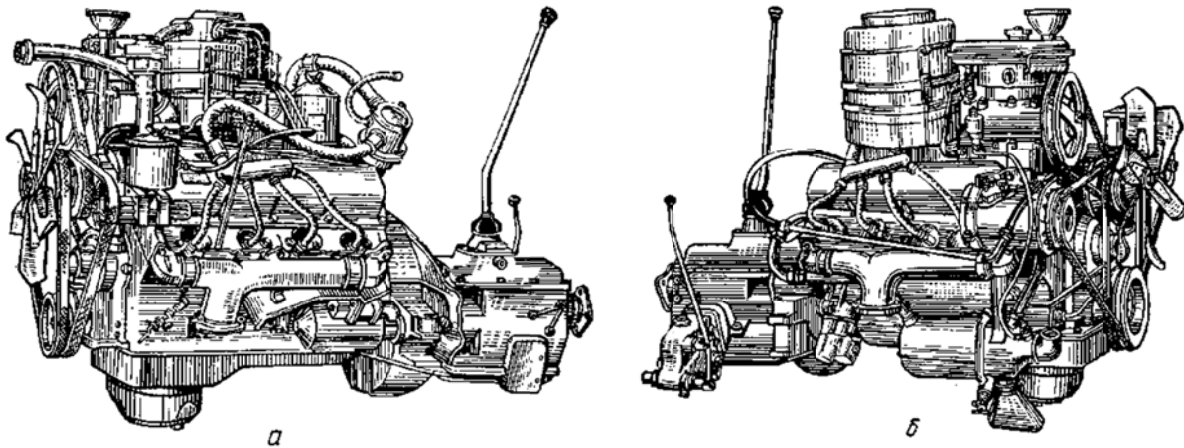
Двигатель ЗИЛ-131: *а* – вид слева; *б* – вид справа
